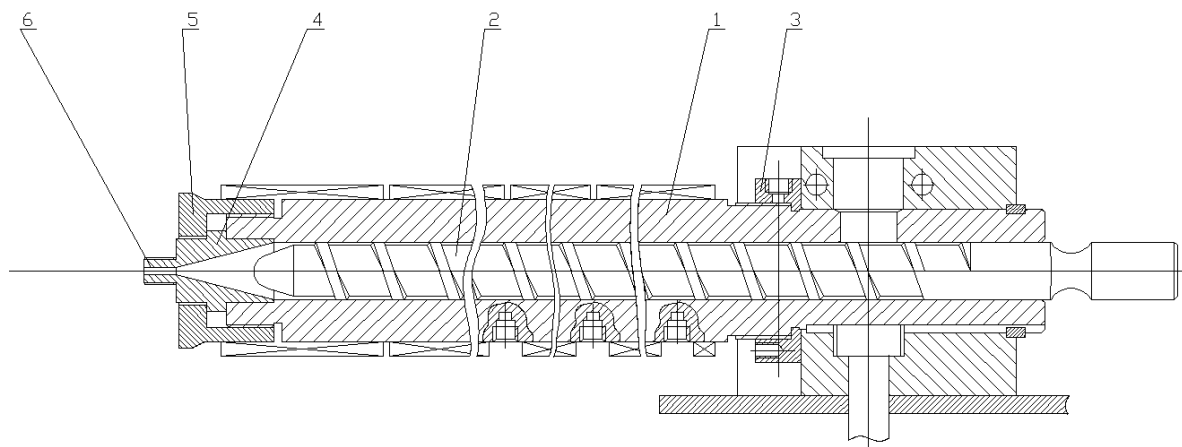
Пластикаційний циліндр з формуючою головкою
